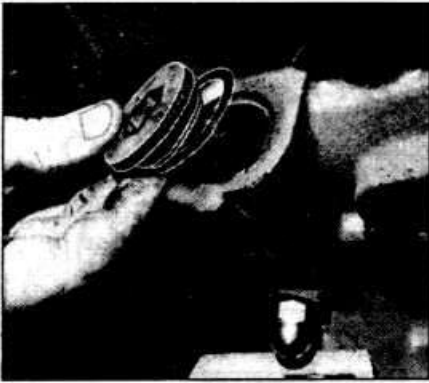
Снятие заглушки корпуса масляного насоса и регулировочного кольца
